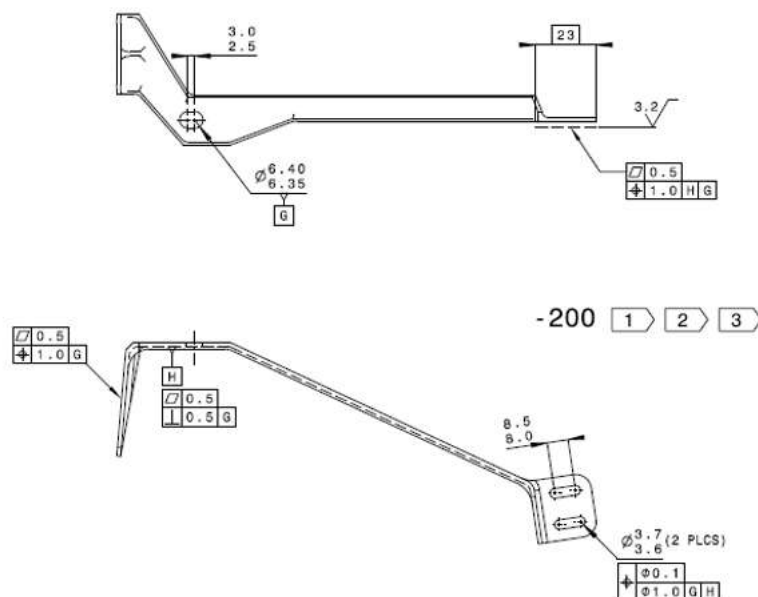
Segmento del CAD drawing fornito da Leonardo SpA
